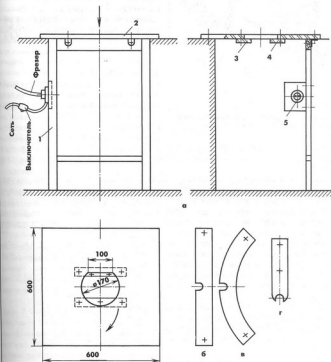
Стол для фрезерования с нижним расположением шпинделя (а) и направляющие линейки для фрезерования (б–г); 1 – опора, 2 – крышка, 3, 4 – опорные планки, 5 – сетевая розетка.
